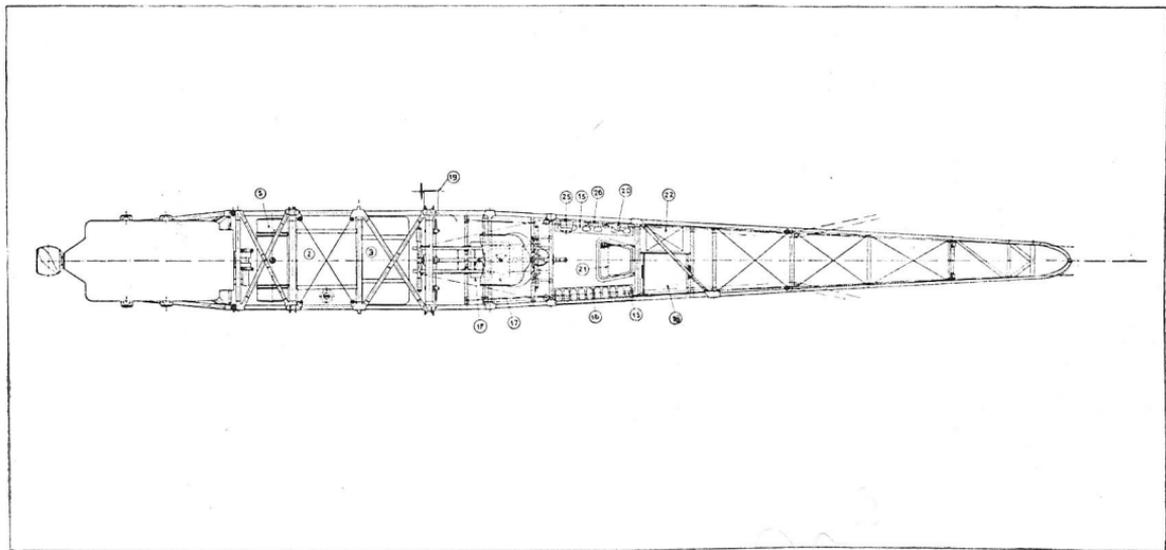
STRUTTURA DELLA FUSOLIERA CON SISTEMAZIONI - PIANTA
